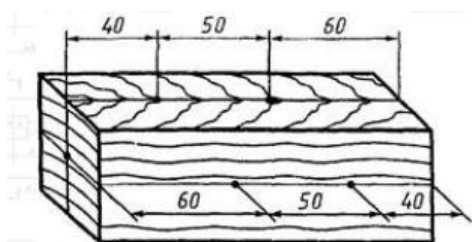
Схема розмітки зразка для загвинчування шурупів
